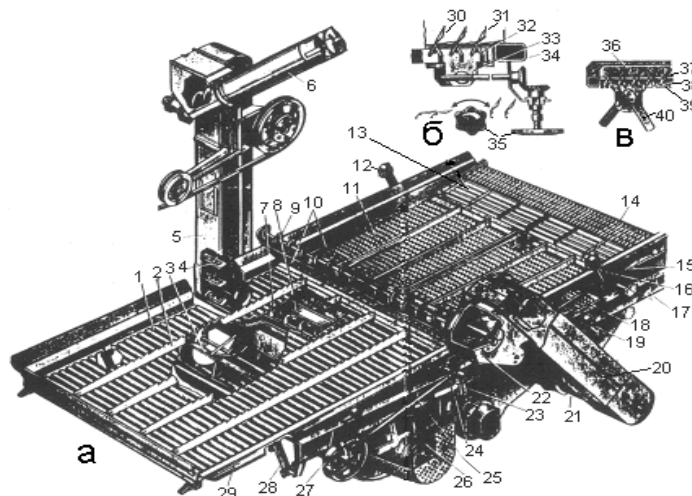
Система очистки зерноуборочного комбайна «Дон-1500»: а – общий вид; б – механизм регулирования открытия жалюзи решет; в – механизм открытия пластин удлинителя; 1 – транспортная доска; 2 – гребенка; 3 – вентилятор; 4 – скребки; 5 и 20 – элеваторы; 6, 7, 10 и 21 – шнеки; 8 – дно решетного стана; 10 – пальцевая решетка; 11 и 18 – решета; 12, 16, 110 и 28 – подвески; 13 – удлинитель; 14 – надставка; 15 и 17 – рамы; 22 – домолачивающее устройство; 23 и 40 – рычаги; 24, 31 и 37 – оси; 25 – шатун; 26 – шкив; 27 – колебательный вал; 210 – уплотнитель; 30 – жалюзи; 32 и 38 – колено; 33 и 310 – рейки; 34 – рамка; 35 – маховичок; 36 – пластина.
